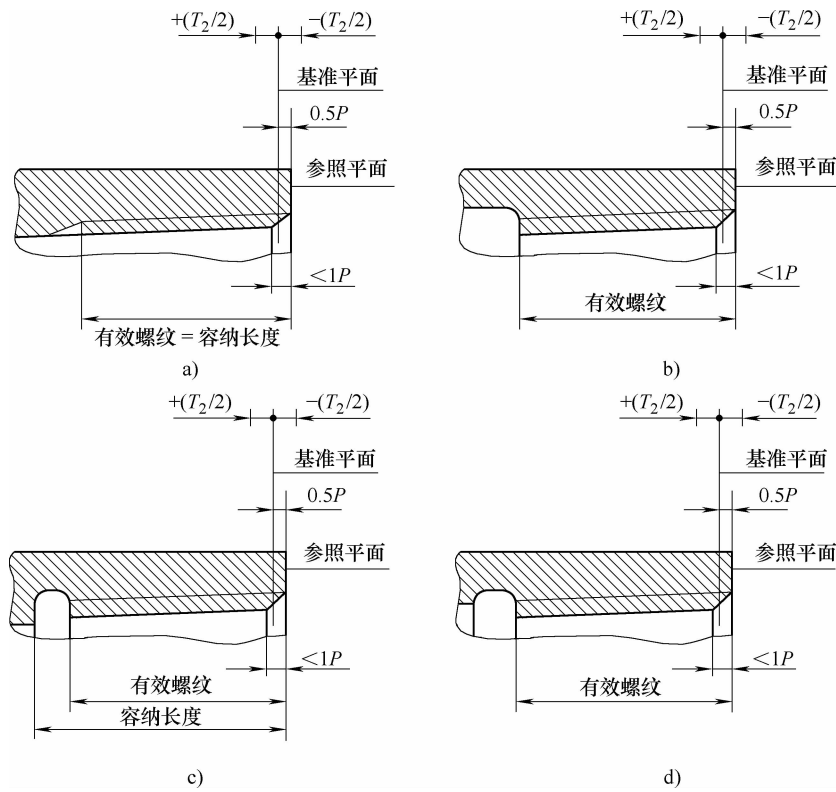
圆锥内螺纹各主要尺寸的分布位置
